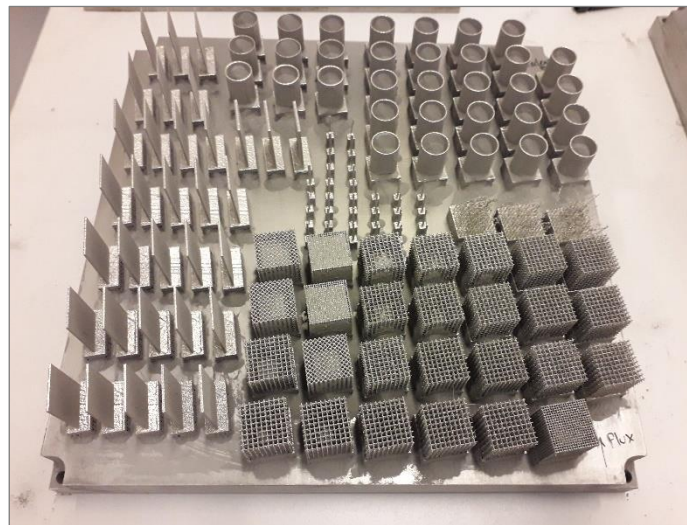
Exemple de plateau de fabrication, avant décrochage des pièces
